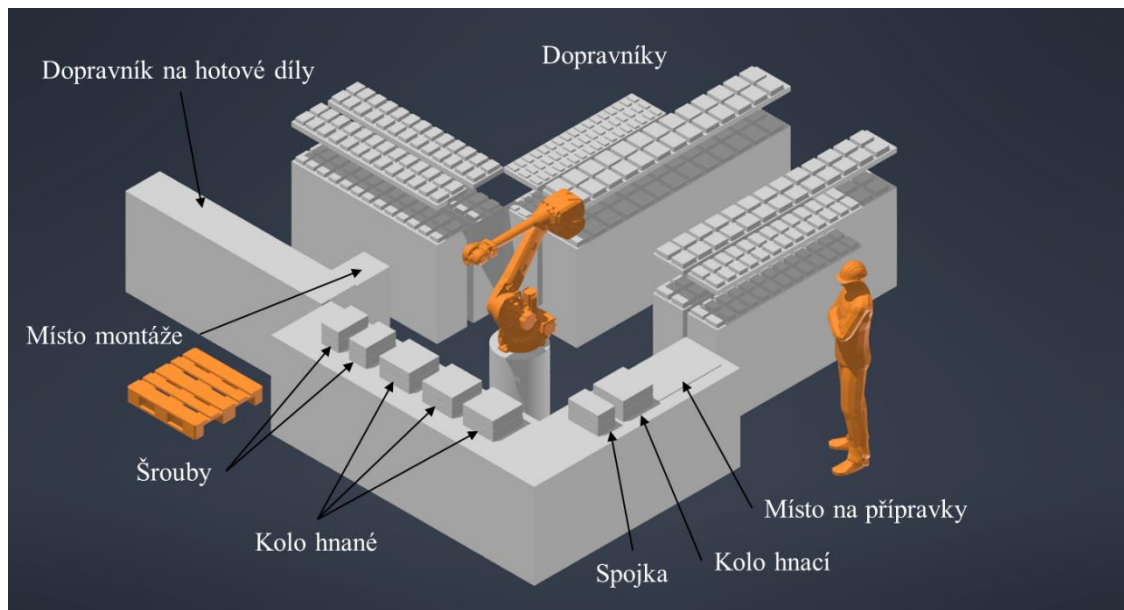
Varianta 1 – Iterace 2 – Hrubý návrh pracoviště – Pohled ze shora
